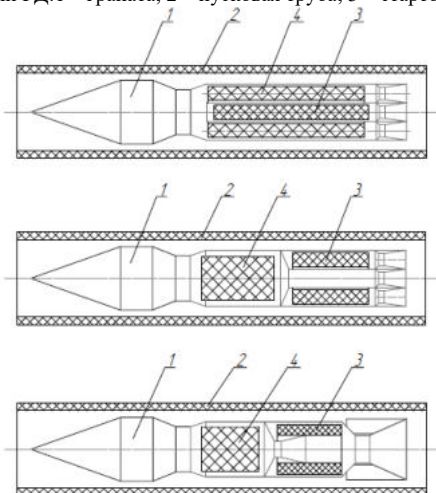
Двухкамерный двухрежимный РД: 1 – граната; 2 – пусковая труба; 3 – стартовый РД; 4 – маршевый РД.
